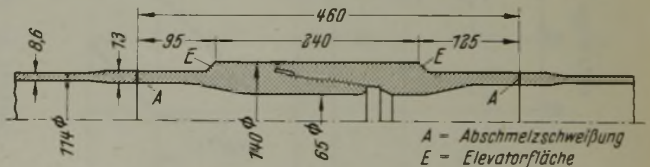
Rohrverbindung mit angeschweißtem Tool Joint.
